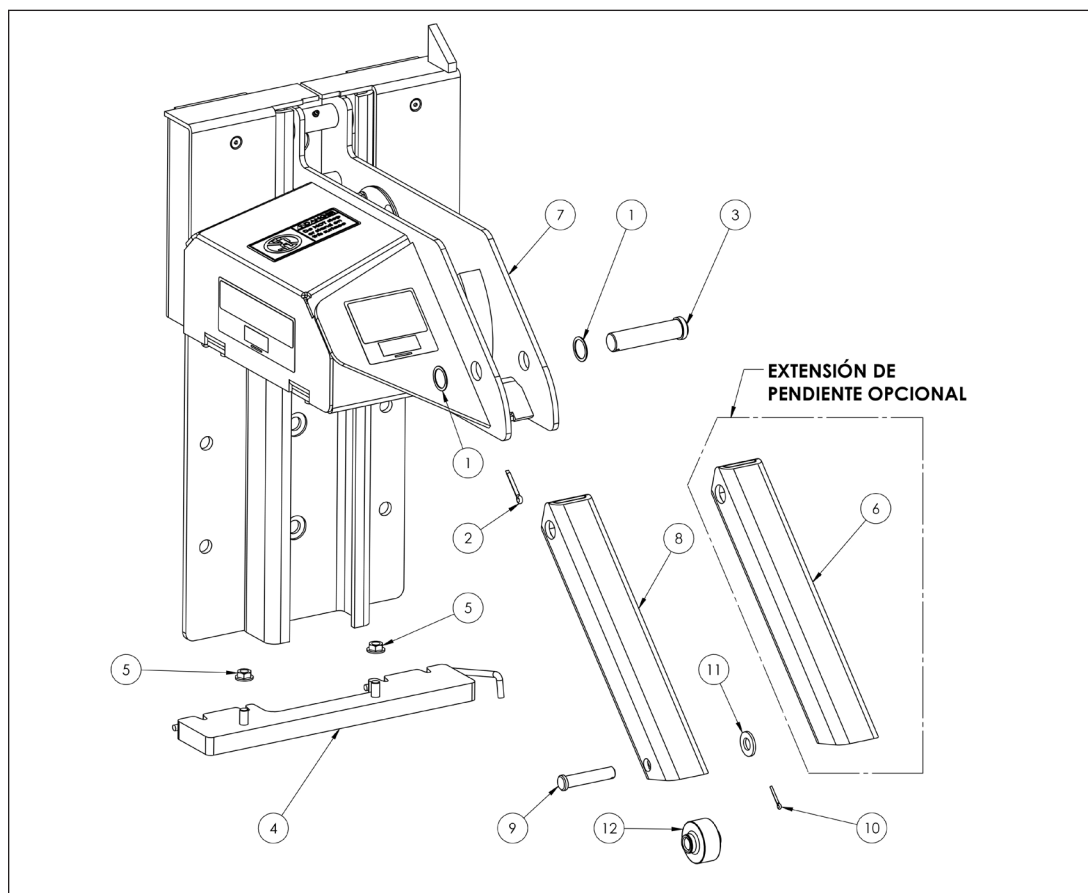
FIGURA AS—CONJUNTO DE EXTENSIÓN DE PENDIENTES
